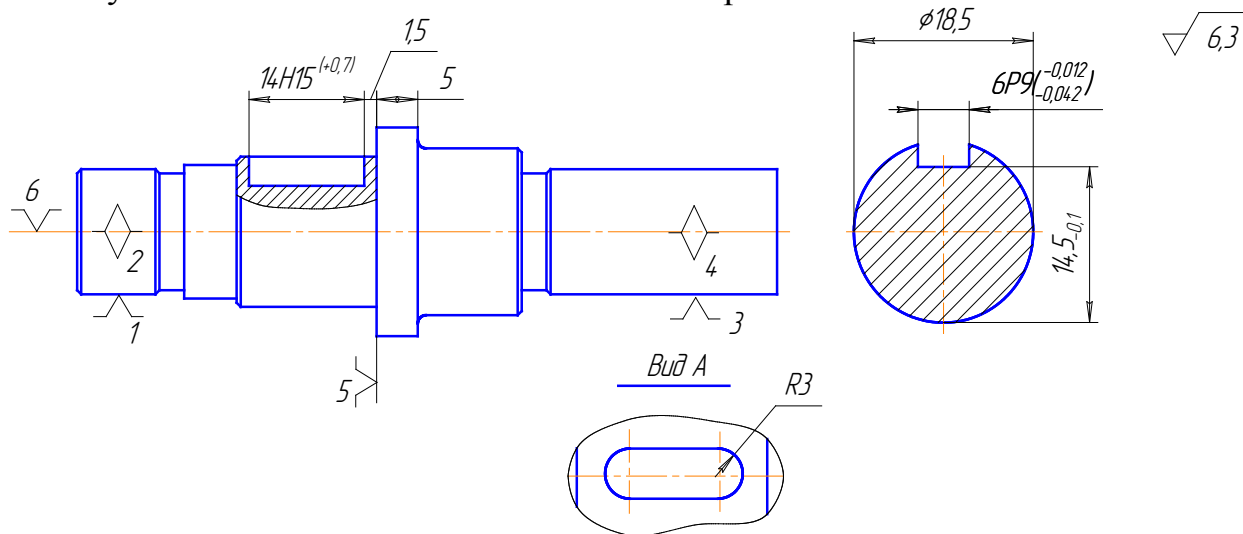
Ескіз на фрезерування паза 6P9^{-0,012}_{-0,042} вала КМ2134.АФ1-39-401
